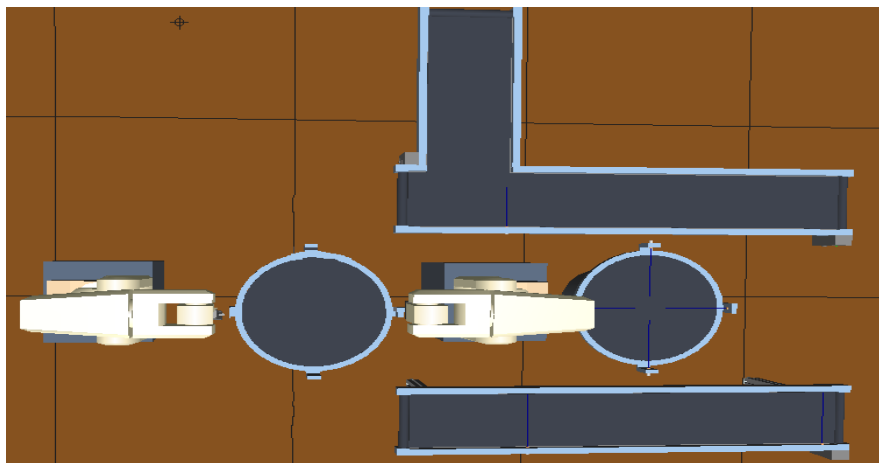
Simulación del sistema del proceso del Ensamblaje y Soldadura de la tarjeta impresa, vista desde arriba (Cambio de la planta).
